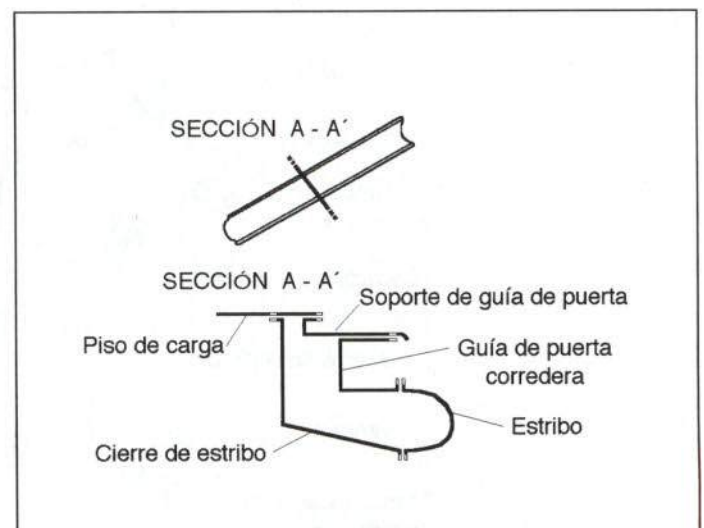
Accesibilidad del estribo bajo la puerta lateral
